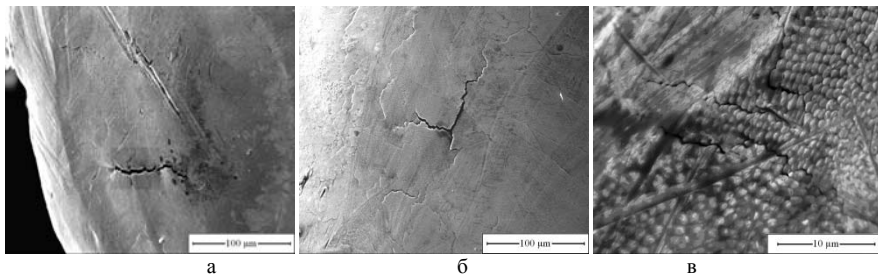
Трещины в сварном соединении сплава 29НК и стали 12Х18Н10Т
